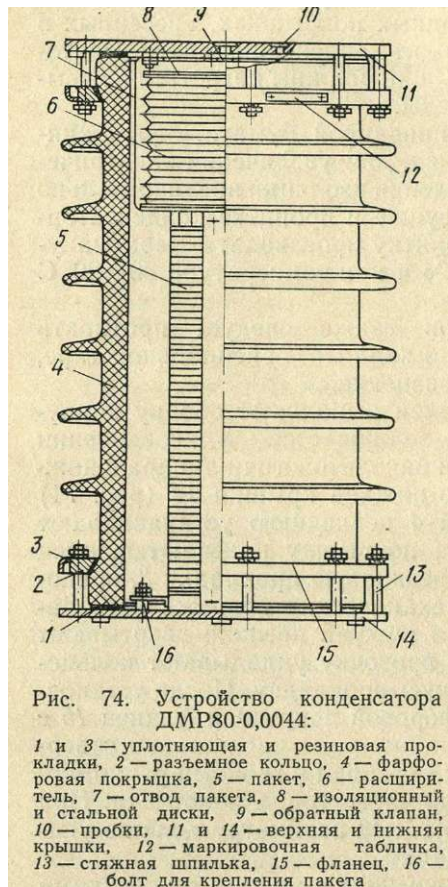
Устройство конденсатора ДМР80-0,0044:
